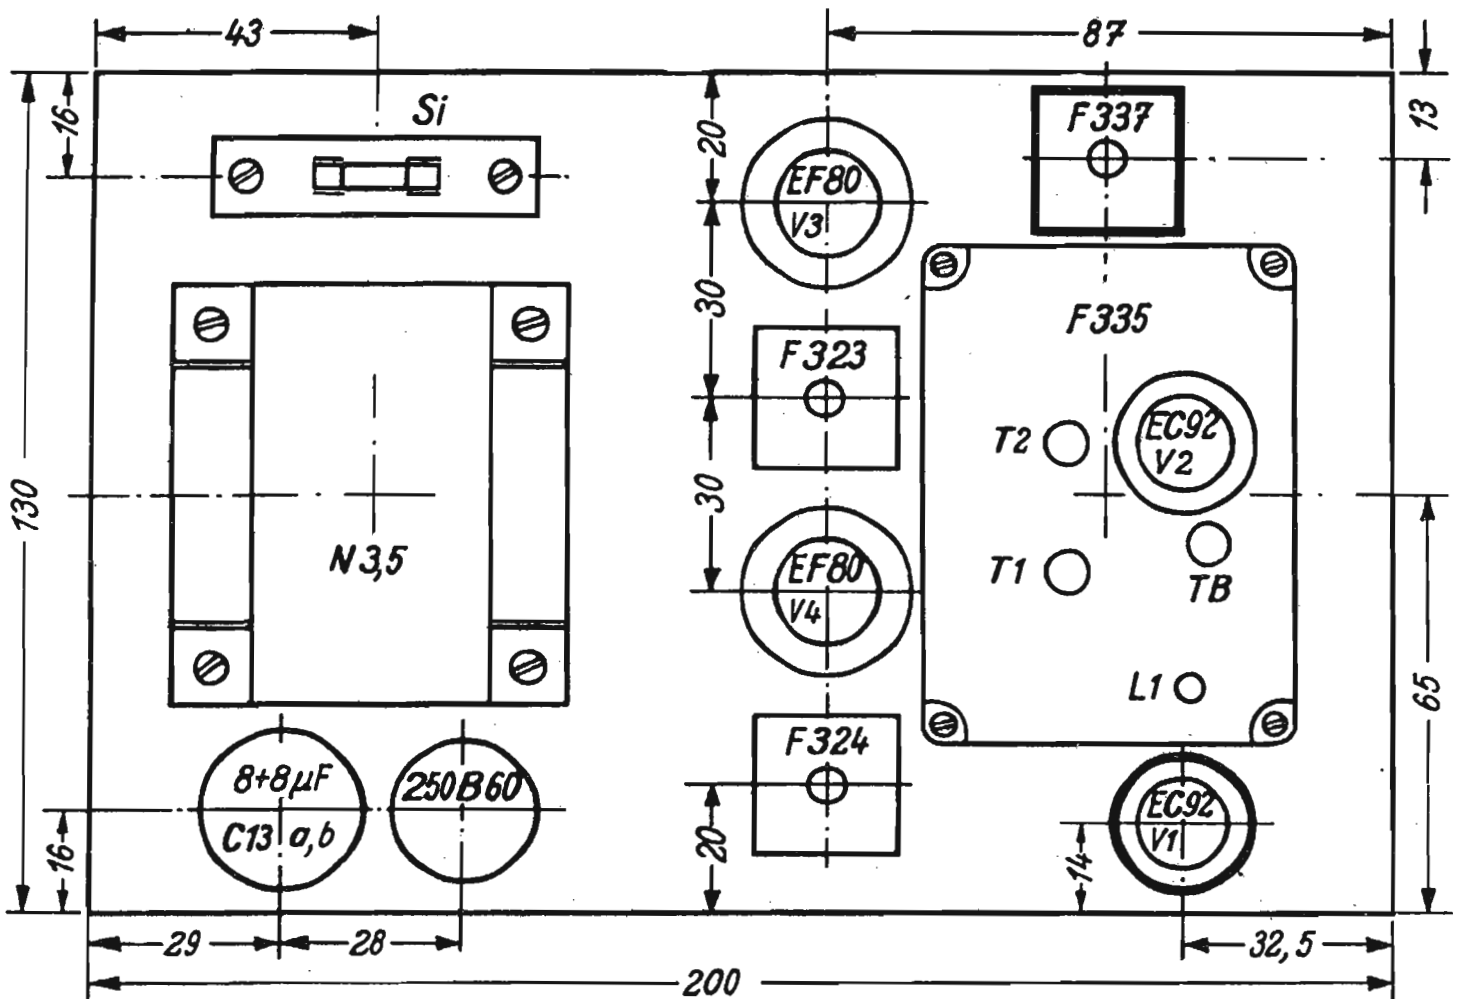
Disposizione delle singole parti sulla piastra di montaggio.
